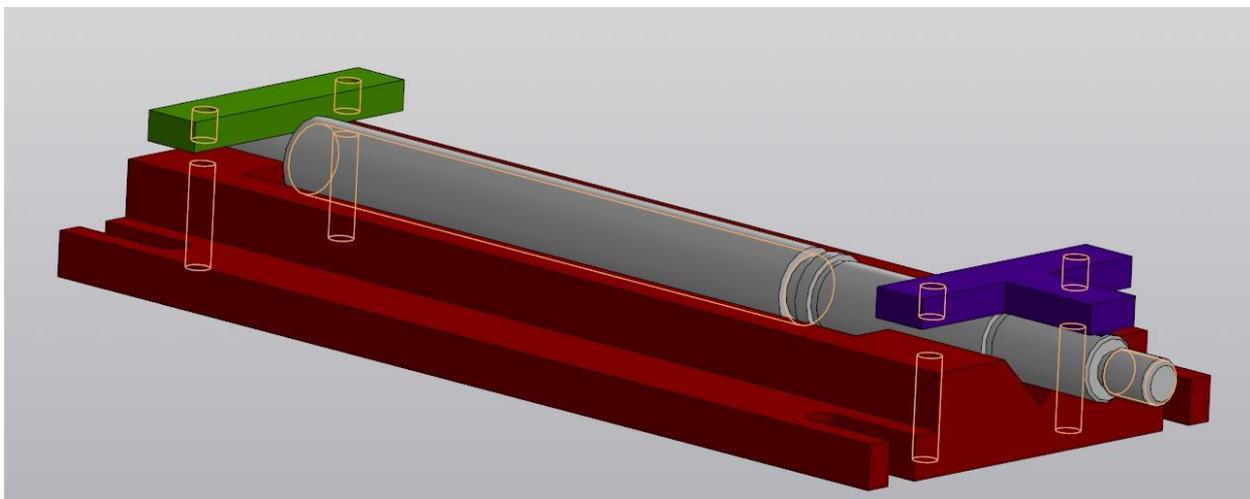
3D – модель приспособления для фрезерной чистовой операции
